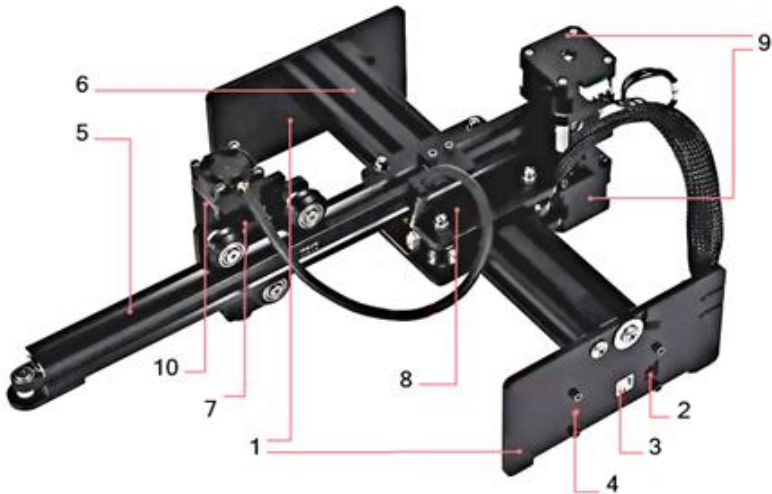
Основні вузли лазерного верстата NEJE Master 2S:
